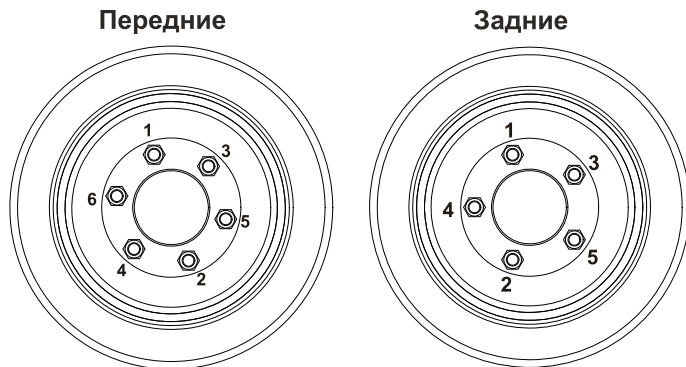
Последовательность затяжки гайки крепления колеса
